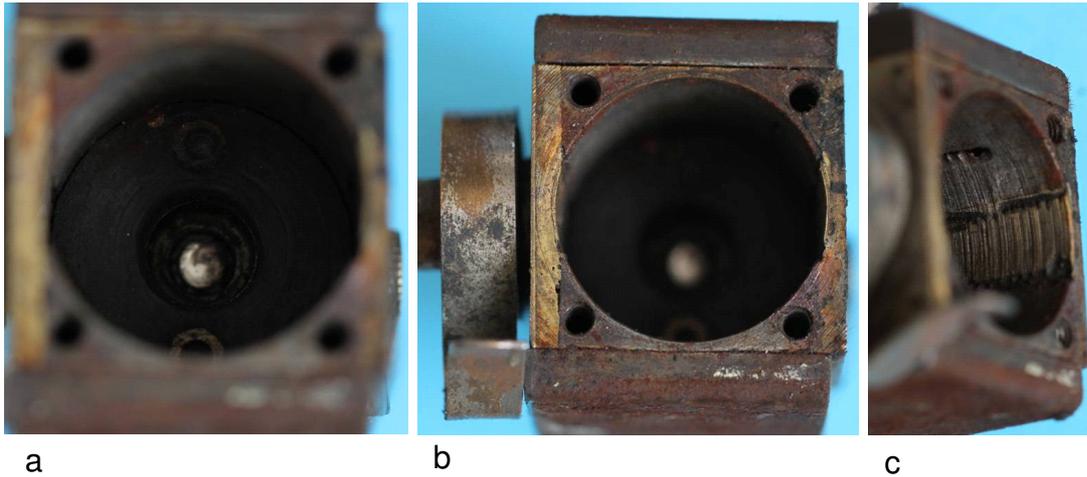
Polgehäuse: a) Federnder Schleifkontakt im Gehäuseboden, b) Gewindebohrungen zur Befestigung des Lagerhalses, c) Drehriefen auf dem Polschuh und der Pollückenabdeckung
